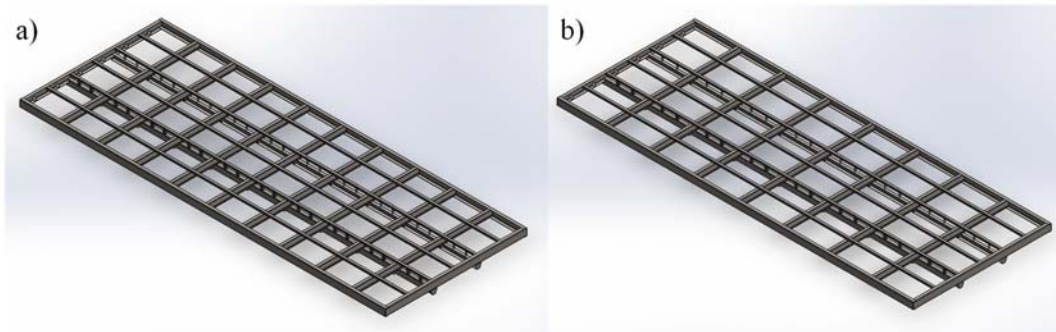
Ejemplo de cómo se puede modificar la cantidad de teleras en la estructura. a) Carrocería con 9 teleras; b) Carrocería con 7 teleras.
